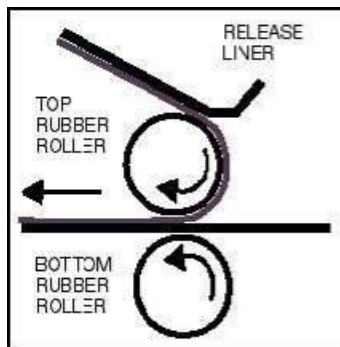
(Покрывающий слой – Верхний резиновый валик – Нижний резиновый валик)
